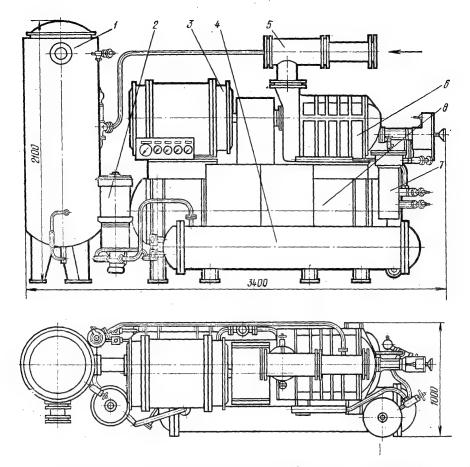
Судовой винтовой компрессорный агрегат 5ВХ-350/5ФС:
